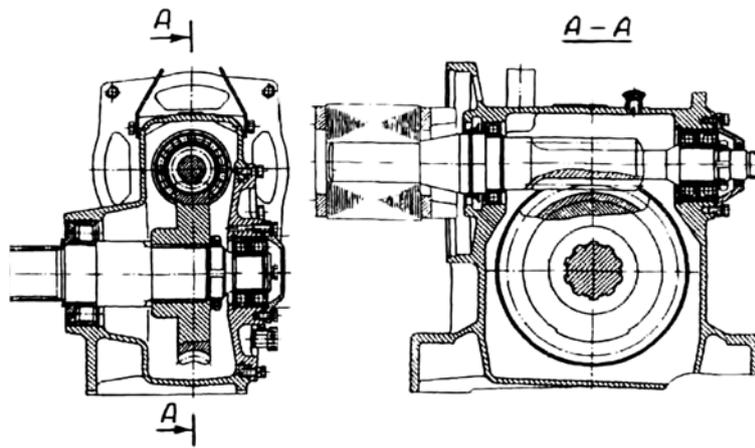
Редуктор с верхним расположением цилиндрического червяка
